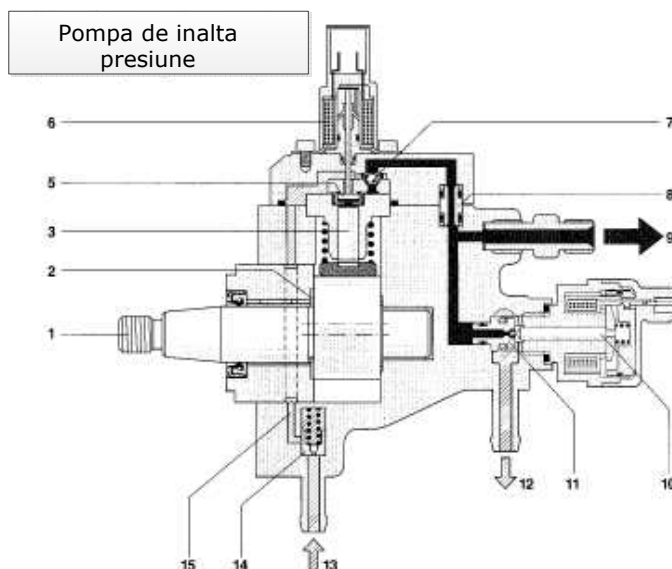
Pompa de înaltă presiune radială cu două pistoane. 1-Ax rotație; 2-Cama dublă; 3-Piston; 4-Carcasa de aluminiu; 5-Ventil admisie; 6-Element acționare ventil; 7-Ventil distribuție; 8-Piesă etanșare; 9-Ieșirea de înaltă presiune către rampa comună; 10 Supapă presiune; 11-Electrovalva PCV cu bilă; 12-Ieșire către circuit retur; 13-Alimentare combustibil; 14-Supapă siguranță; 15-Circuit ungere internă
